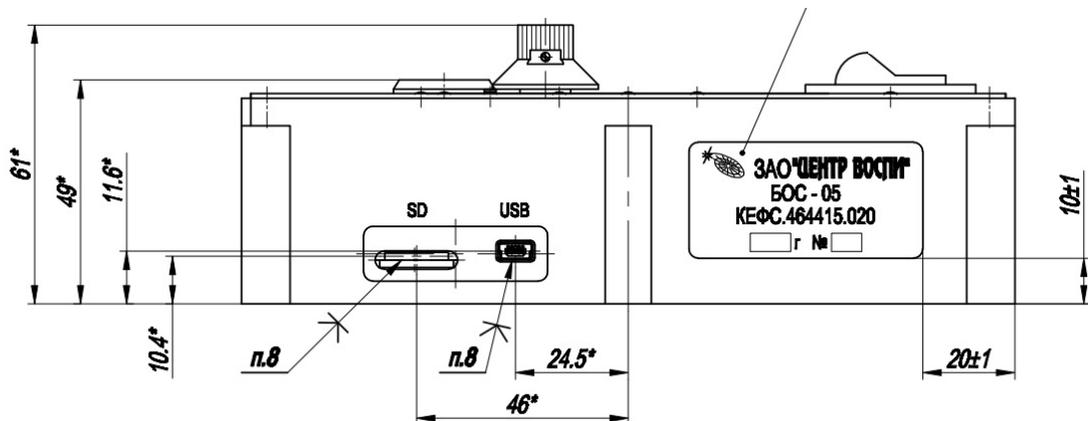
Внешний вид и установка шильдика на БОС-05
